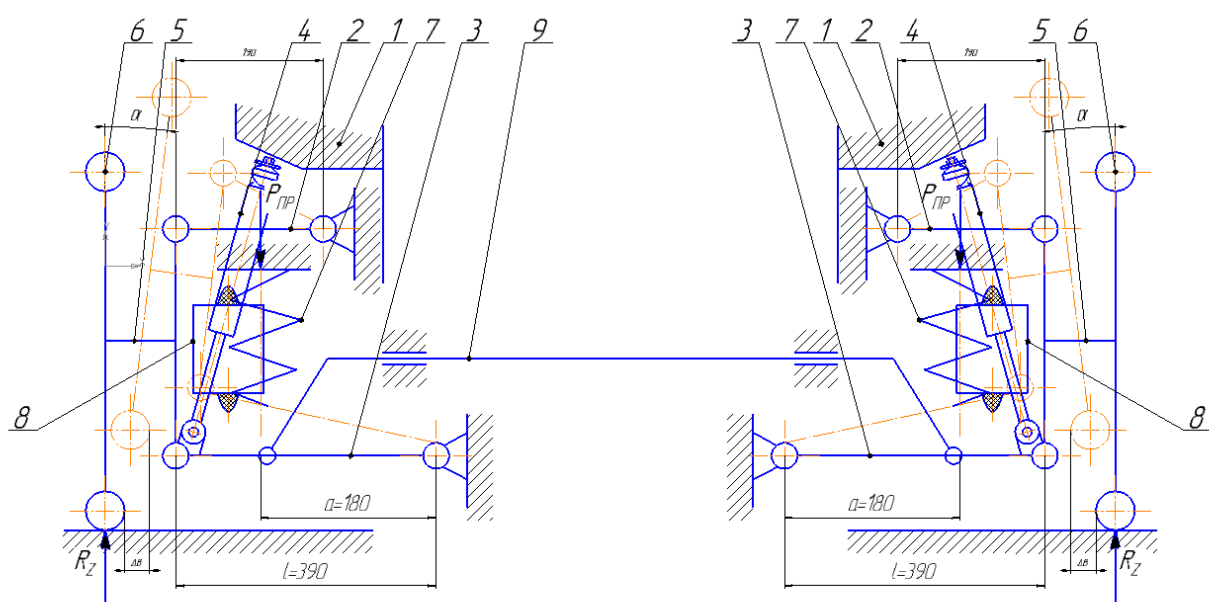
Кинематическая схема разрабатываемой задней независимой подвески на двойных поперечных рычагах: 1 - кузов автомобиля; 2 - верхние рычаги; 3 - нижние рычаги; 4 - амортизаторы; 5 - ступицы колёс; 6 - колёса; 7 - пружины; 8 - буферы отбоя; 9 - стабилизатор поперечной устойчивости
